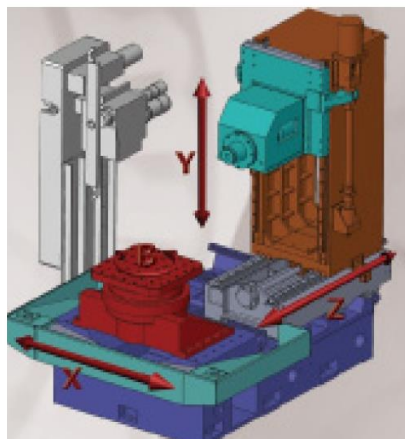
Схема сверлильно-фрезерно-расточного станка с ЧПУ 500HS
